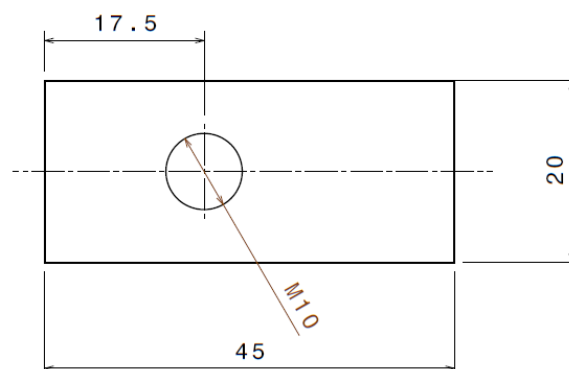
Alzado de la placas de apoyo de mesa sísmica.
